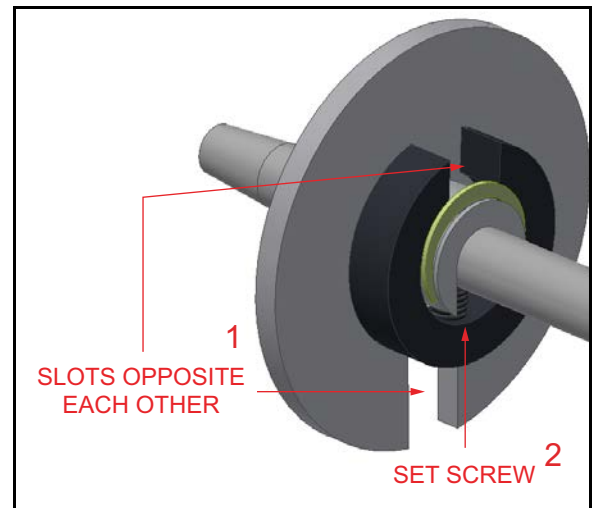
COLLAR GIRADO Y RANURAS OPUESTAS
